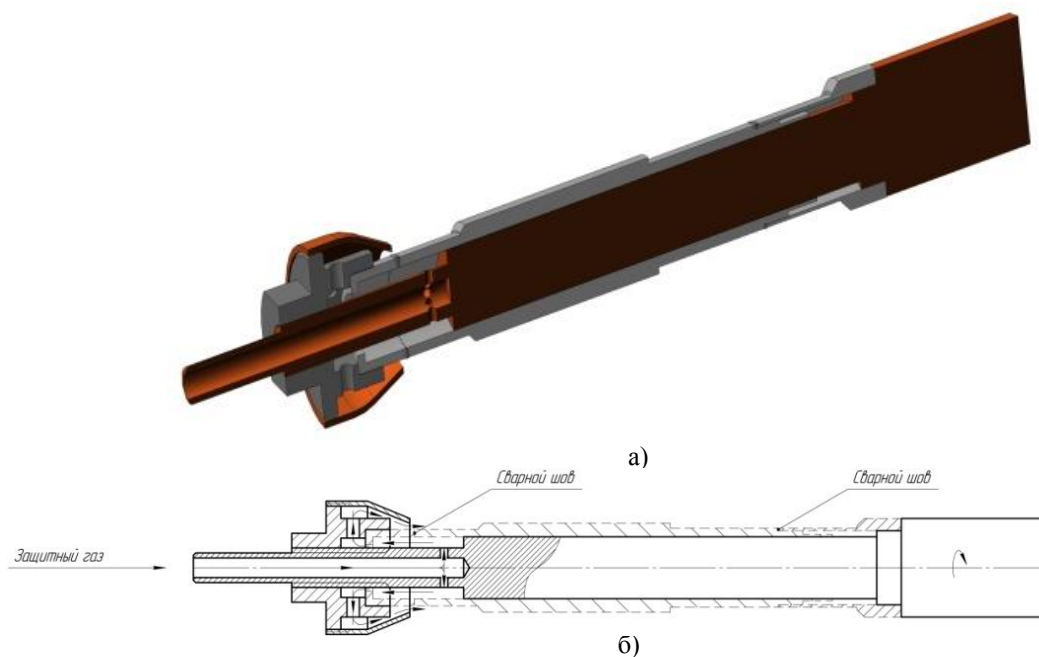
Оправка для лазерной сварки форсунки РД1:
